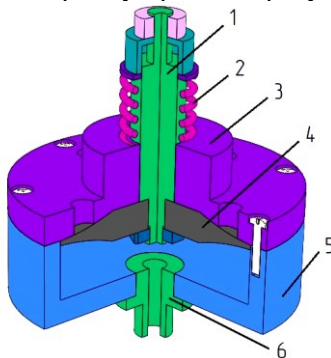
Конструкція зворотного клапану для модуля очистки забруднень потоком твердих частинок: 1 – шток; 2 – пружина; 3 – кришка; 4 – гумовий пелюстковий клапан; 5 – корпус; 6 – штуцер
